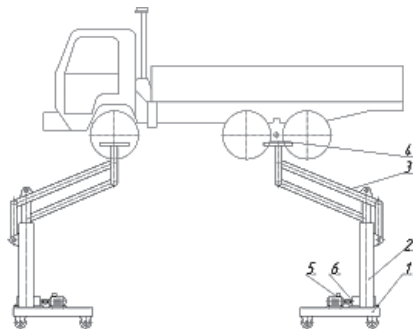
Подъемник передвижной: 1 – рама; 2 – стойка; 3 – стрела грузовая; 4 – сменный захват; 5 – электродвигатель; 6 – червячный редуктор
